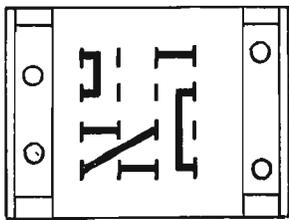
bis. — Câblage du bouchon inverseur, vu côté soudures
